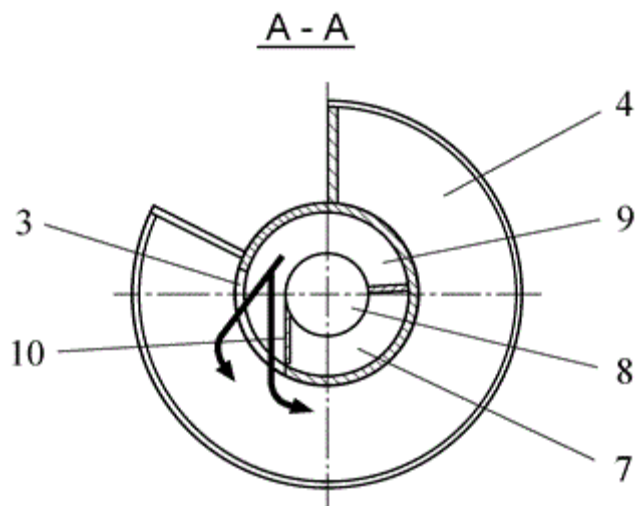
Смеситель №2, разрез А-А: 3 — отверстие; 4 — желоб; 7 — дно загрузочного бункера; 8 — цилиндрическая вставка; 9 — лопасть; 10 — неподвижная заслонка
